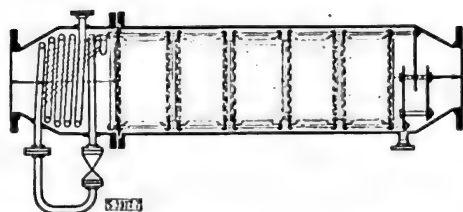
Einspritzkühler mit Vorwärm-schlange
